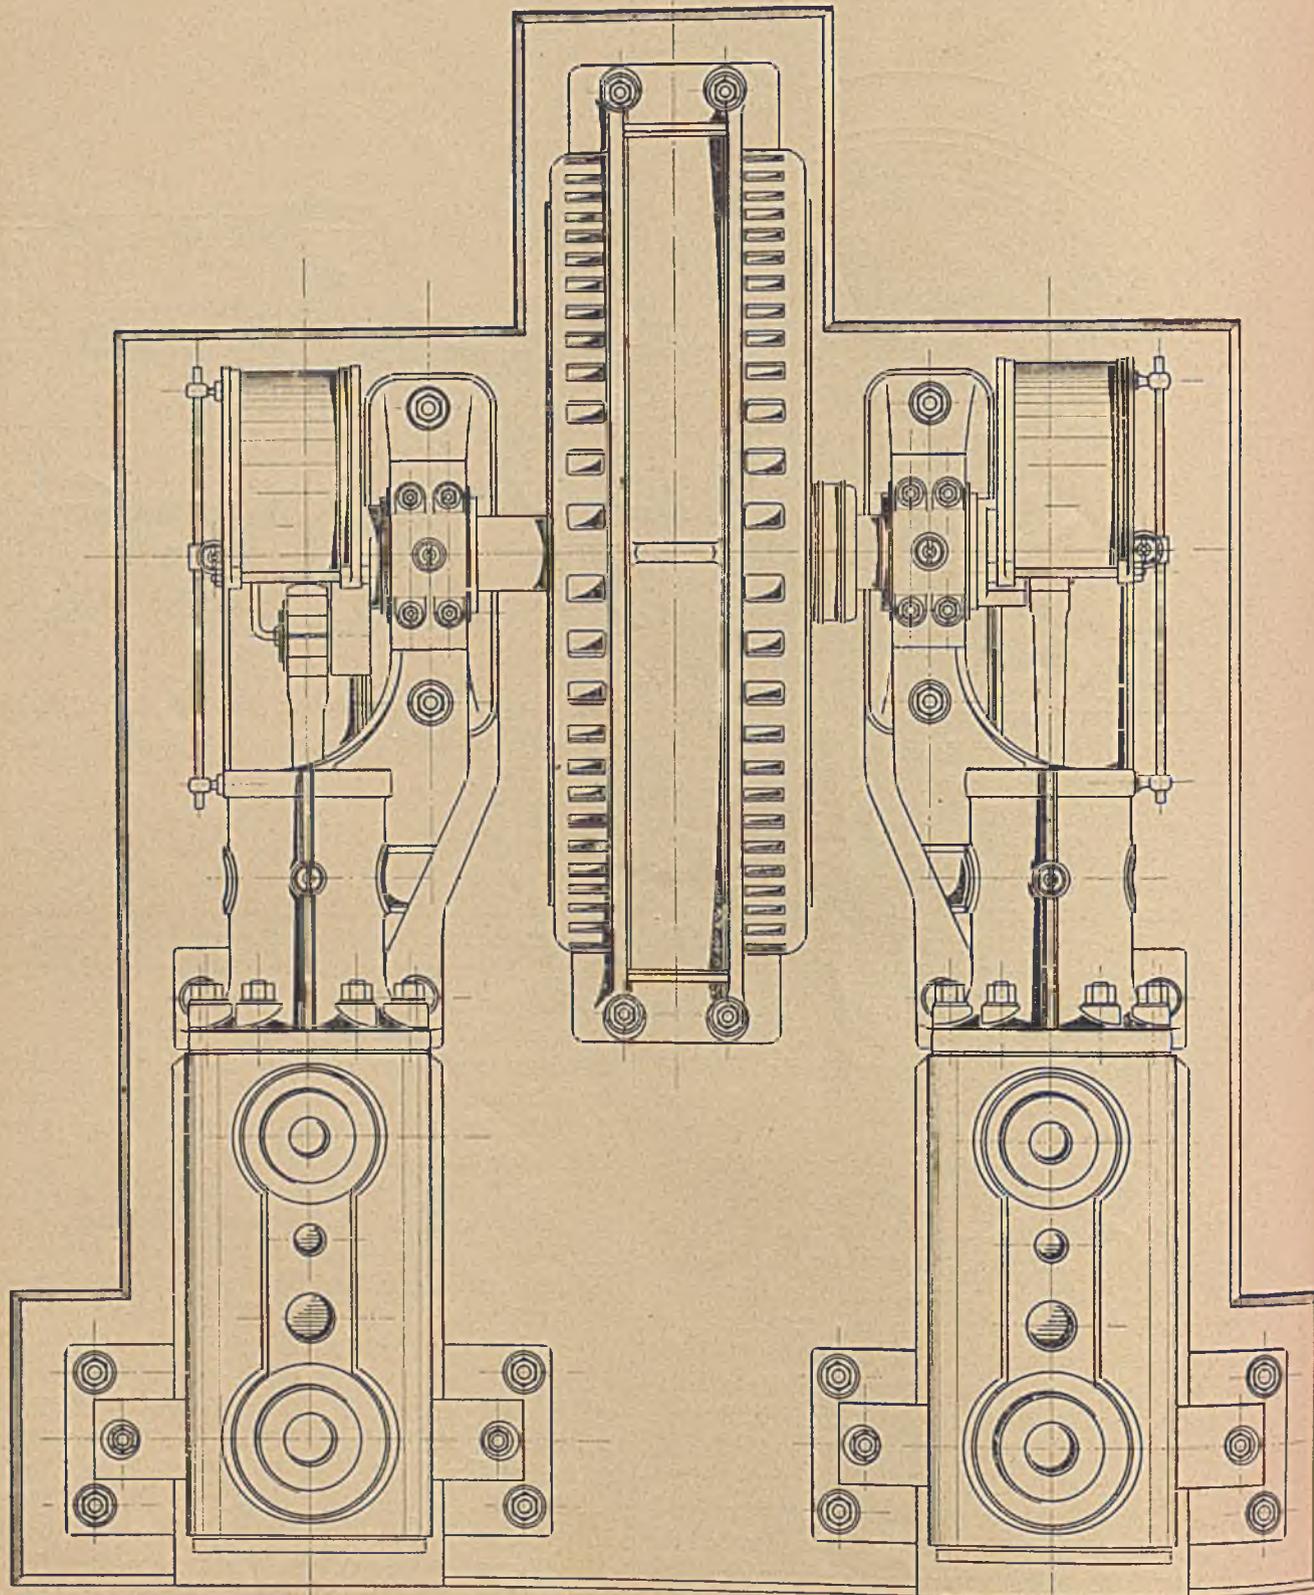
Schnelllaufender Zwillingskompressor von Klein, Schanzlin und Becker mit direktem Elektromotorantrieb. Grundriß.
